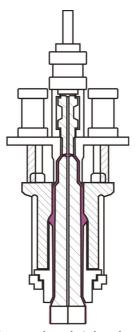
Vista frontal de un cabezal típico de extrusión empleado para la fabricación de preformas.
